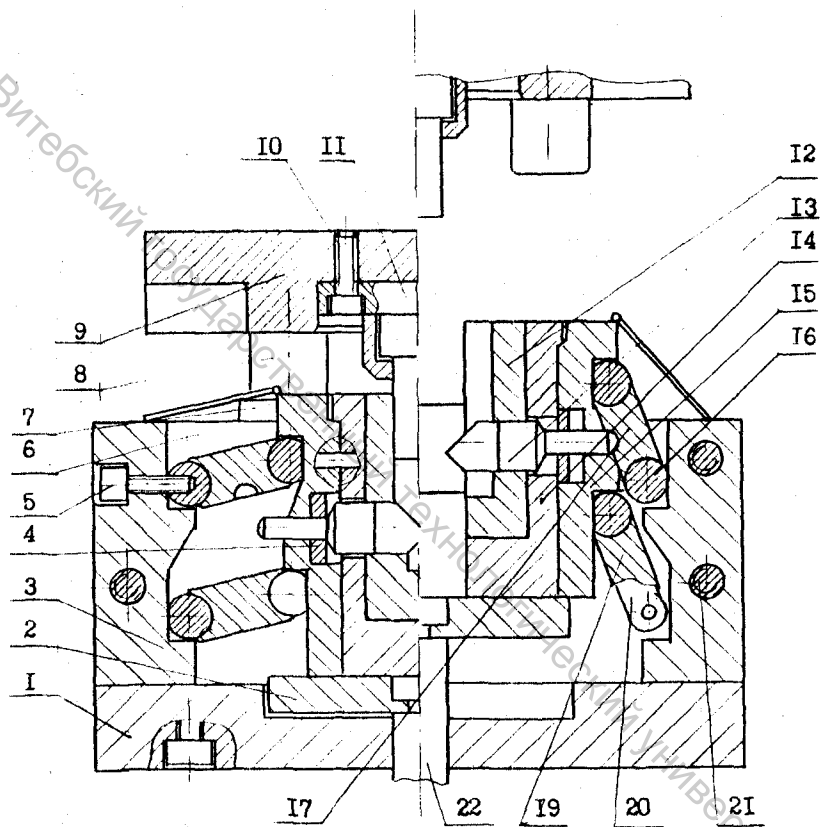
Пакет рычажный с вертикальным разъемом матриц.
